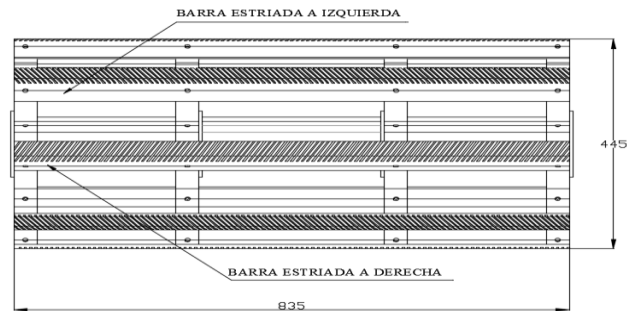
Dimensiones geométricas del cilindro desgranador de barras
